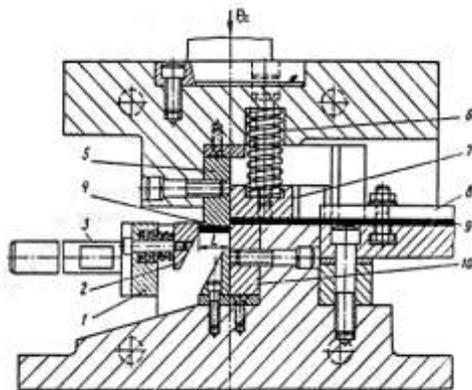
Штамп для отрезки с прижимом: 1 – каретка; 2 – упор; 3 – стержень; 4 – заготовка; 5 – пуансон-нож; 6 – пружина; 7 – прижим; 8 – планки; 9 – полоса (лента); 10 – матрица-нож
